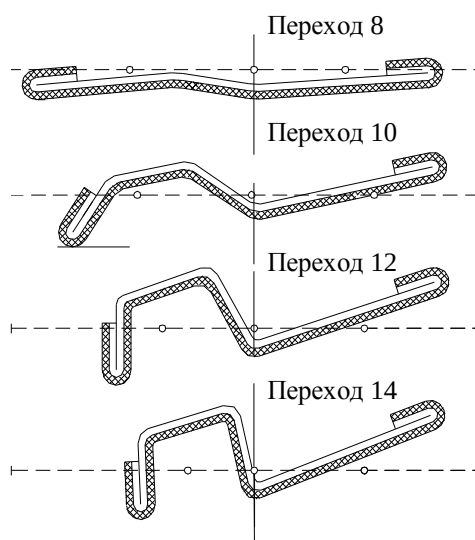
Изготовление профиля из заготовки 145x1,2 мм
